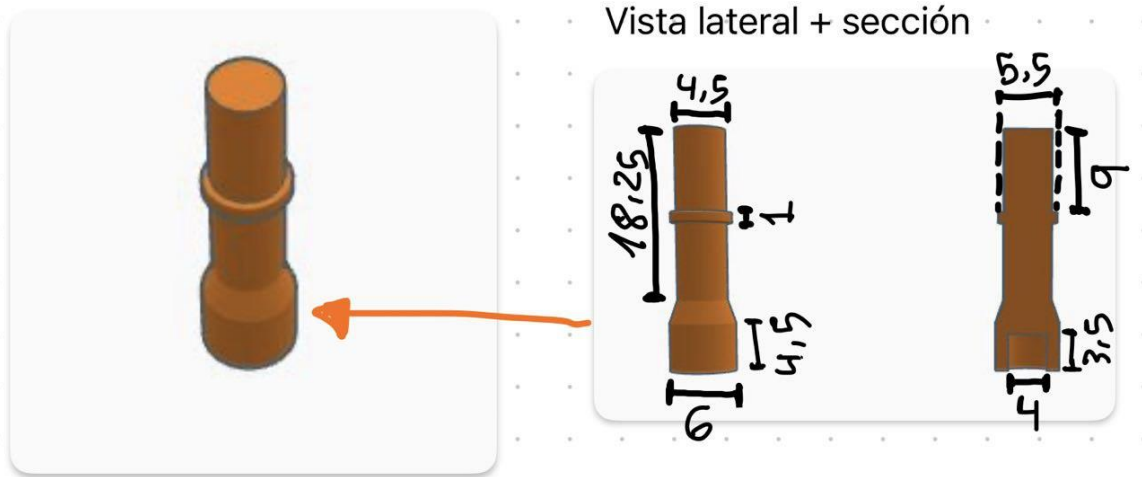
Dimensiones en milímetros del extensor del botón (coloquialmente denominado 'linterna').
